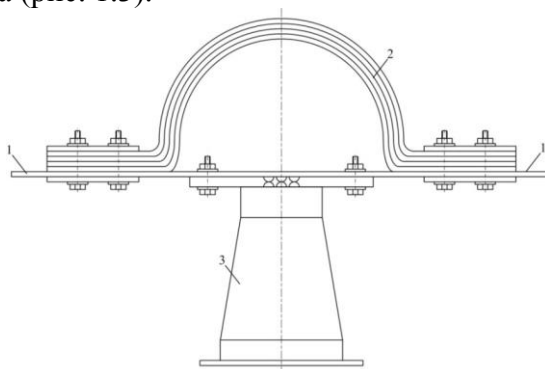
Шинный компенсатор: 1 – шина; 2 – компенсатор; 3 – опорный изолятор; 4 – пружинящая шайба; 5 – накладка
